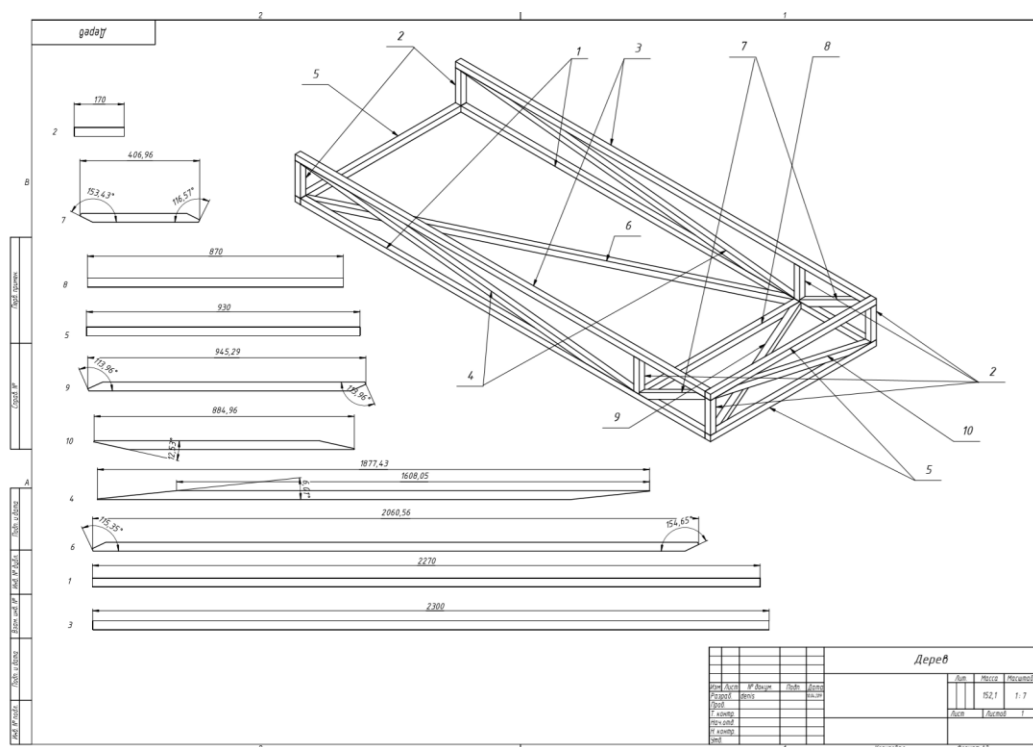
Виробниче креслення нижньої (несучої) частини рами.
